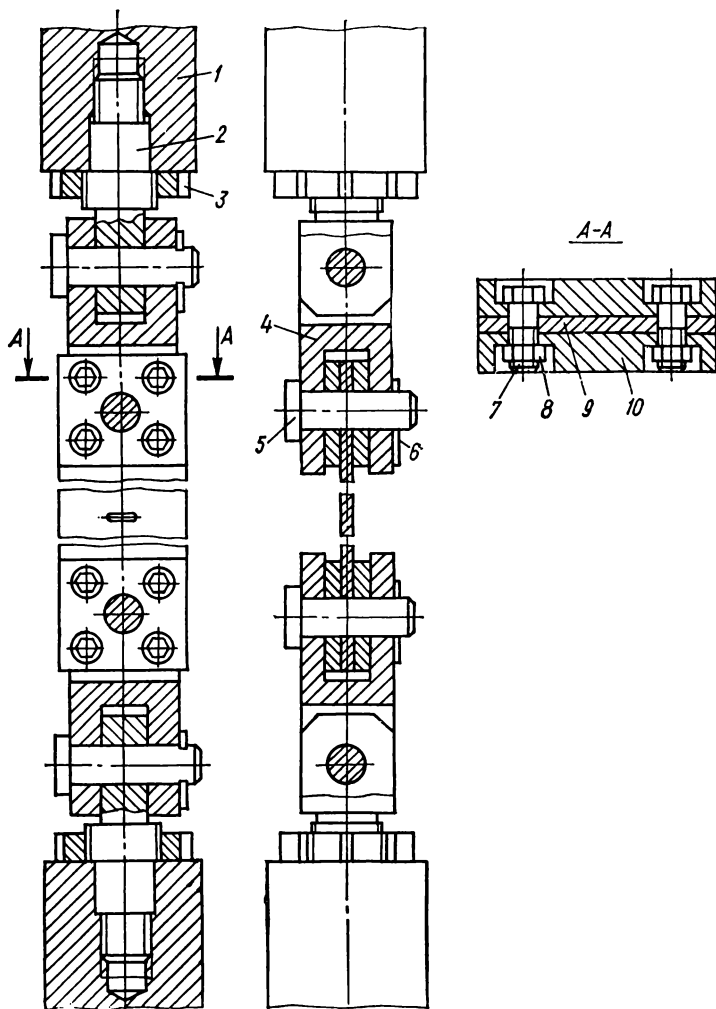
Приспособление с двойным шарниром для крепления образцов с помощью пальца и двойной вилки
